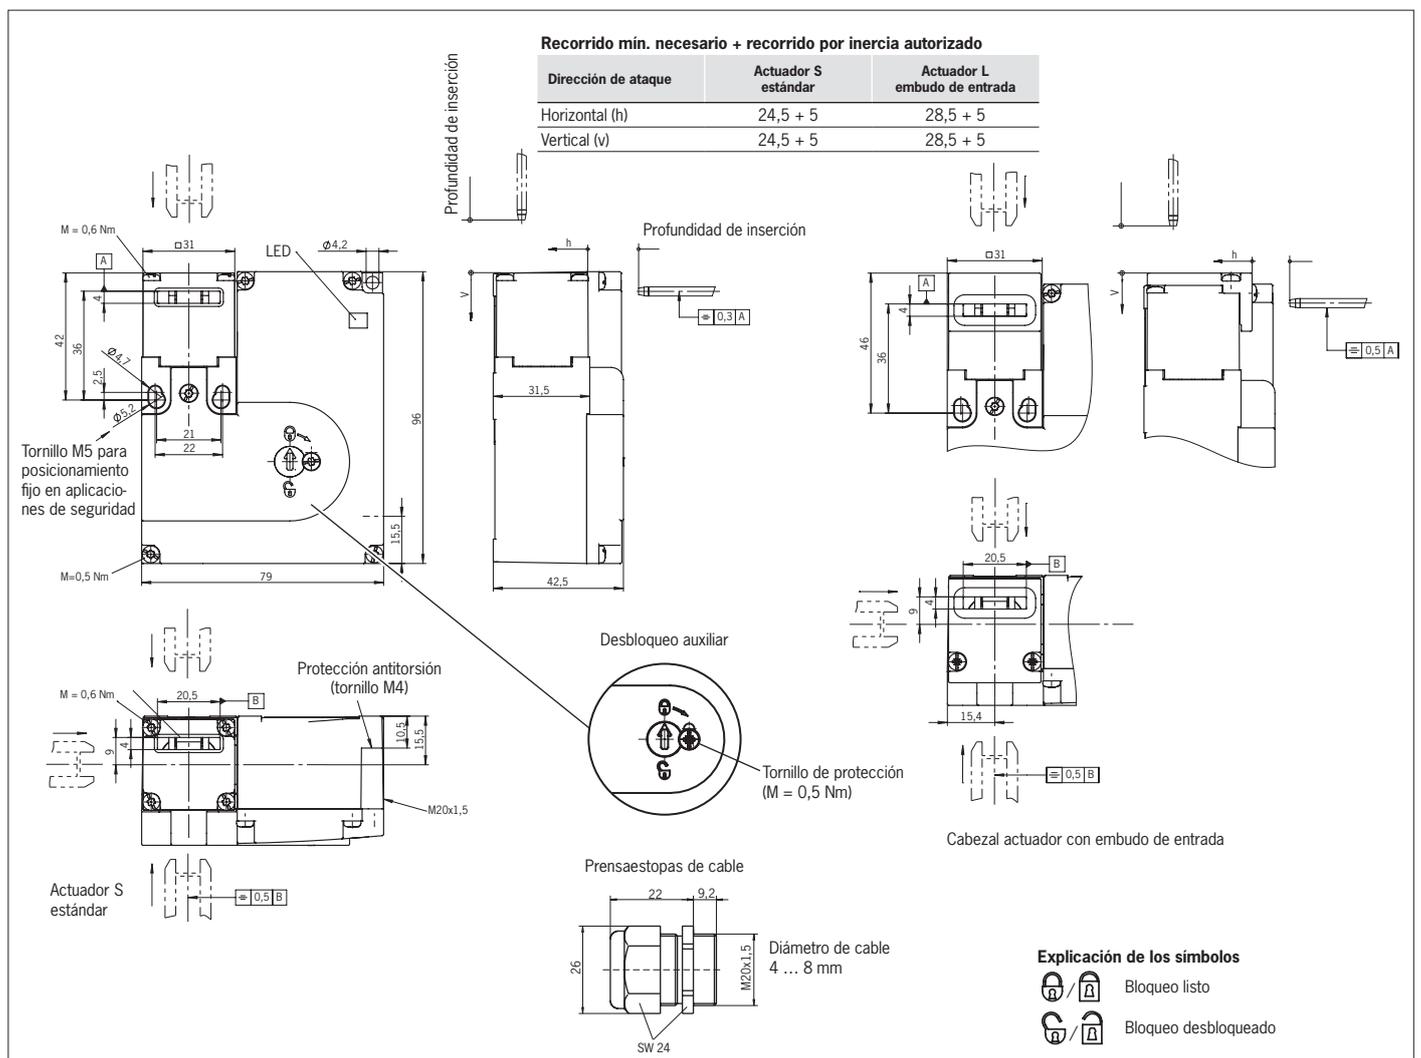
Plano de dimensiones STM Pro sin embudo de entrada y STM Pro con embudo de entrada
